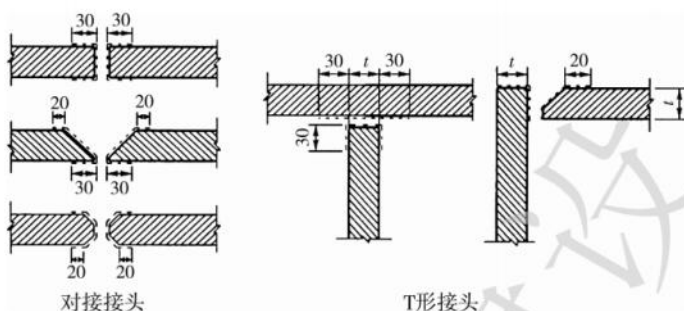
组装前的清除范围(尺寸单位:mm)
